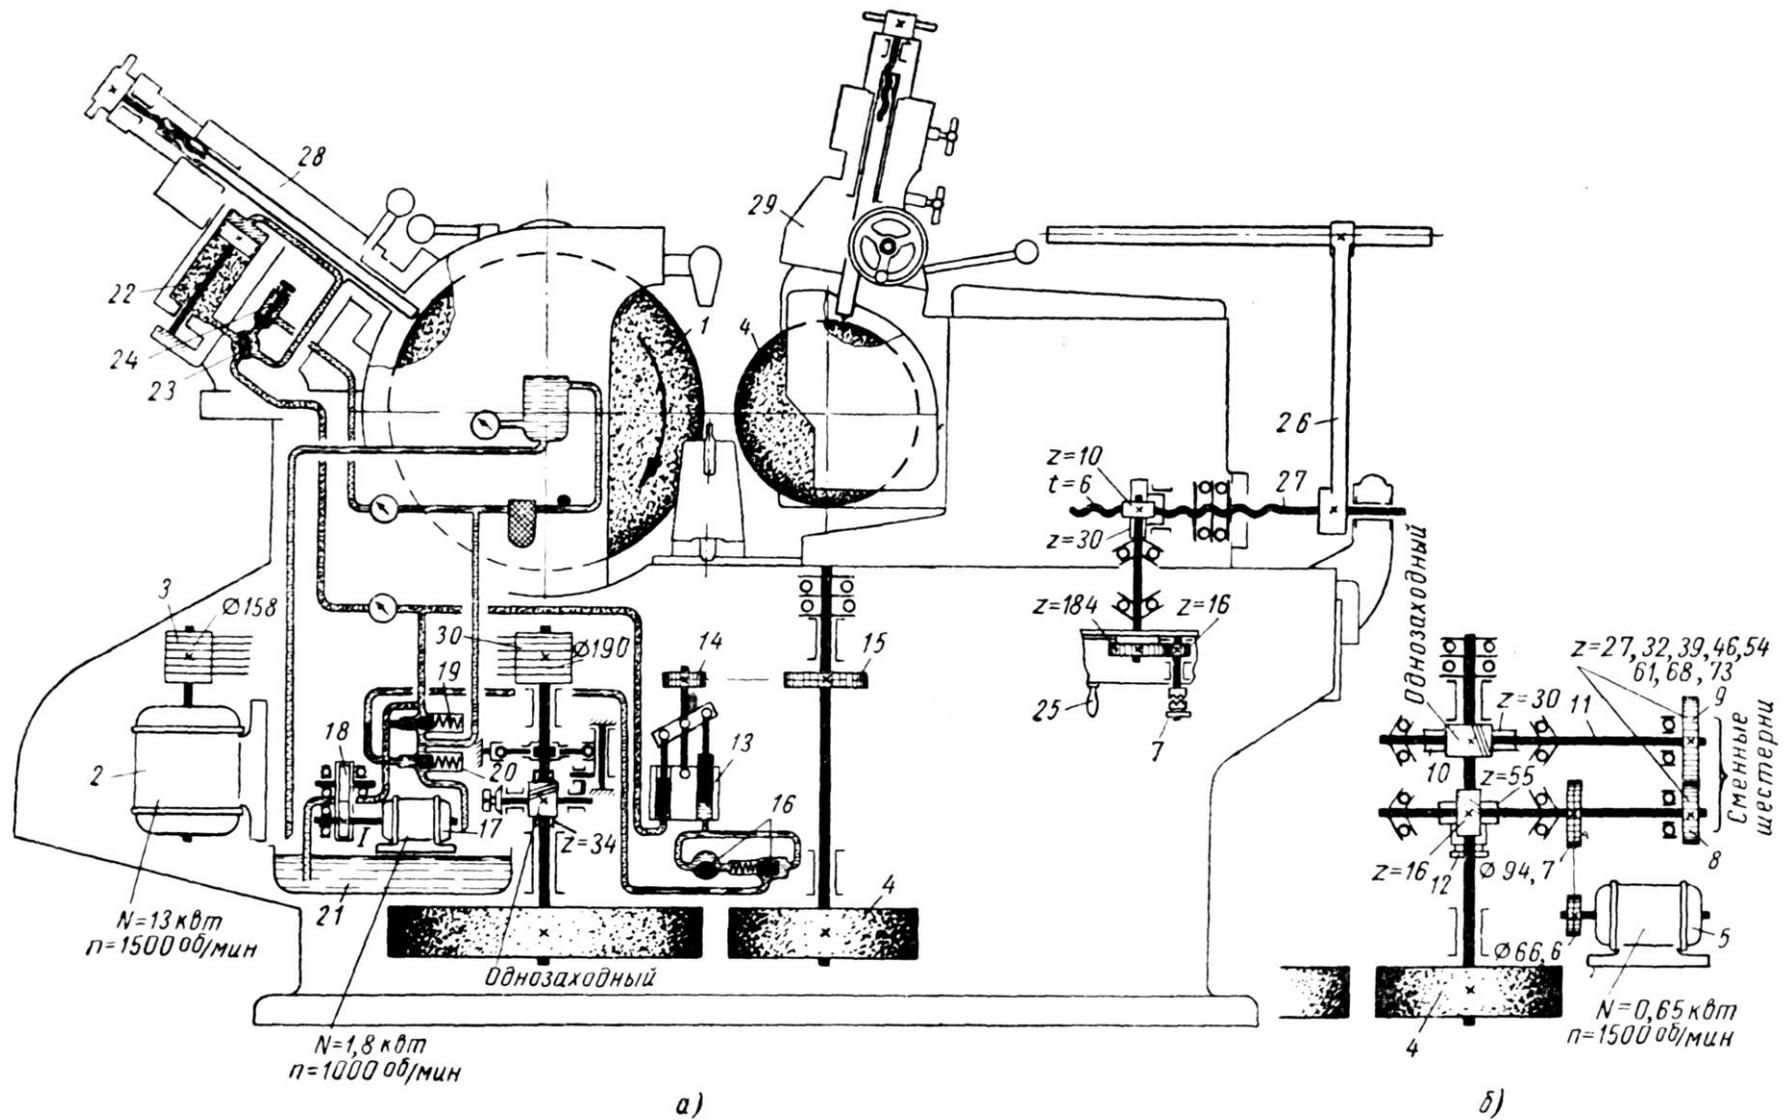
Кинематическая схема бесцентрово-шлифовального станка модели 3180
